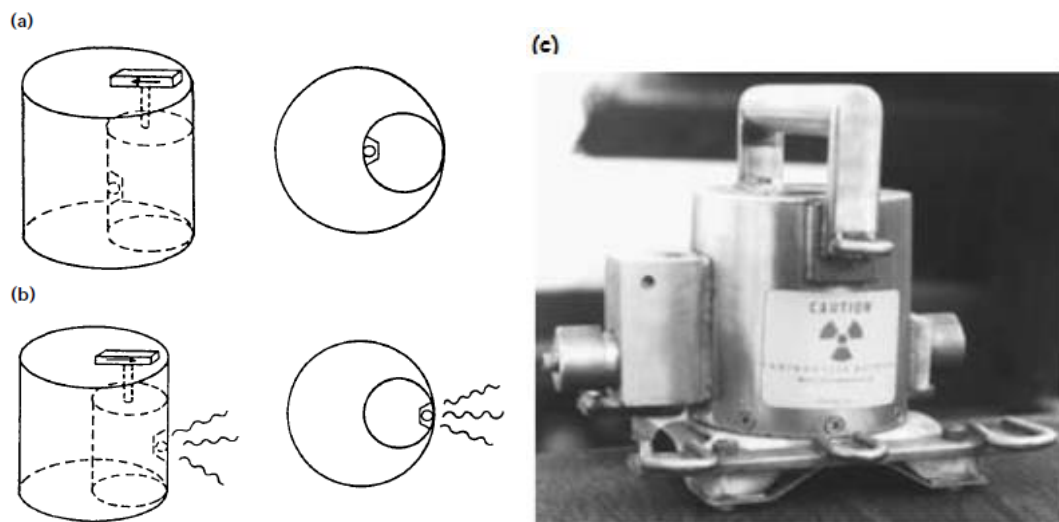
(a) Posición de blindaje, (b) posición de exposición, (c) equipo de exposición ANSI II
